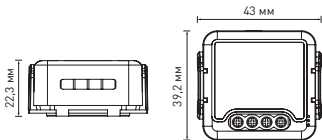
Общий вид и габаритные размеры реле с креплением
